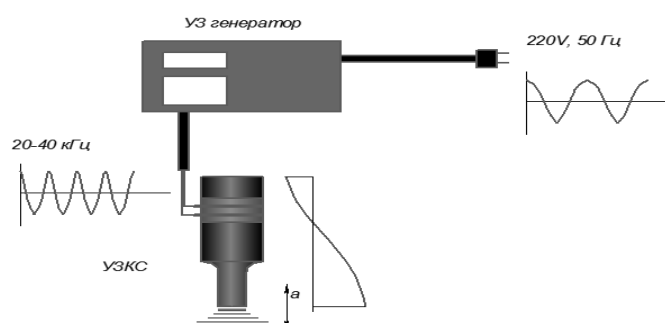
Структурная схема комплексов для ультразвуковой сварки
